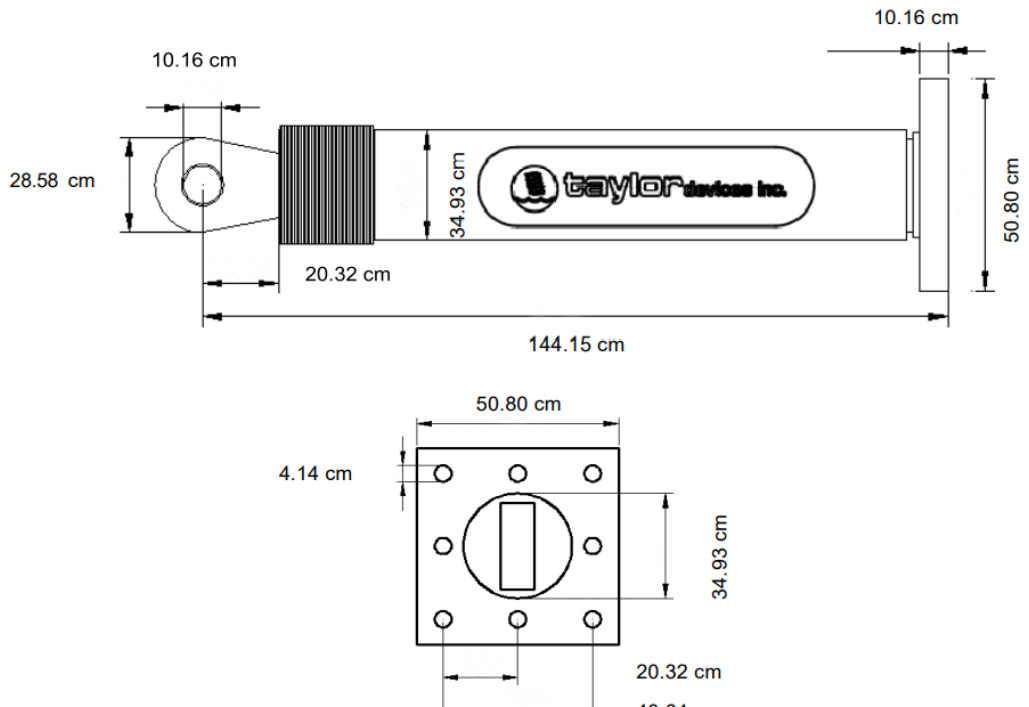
Dimensiones de disipador y placa base de 440 Kip.
